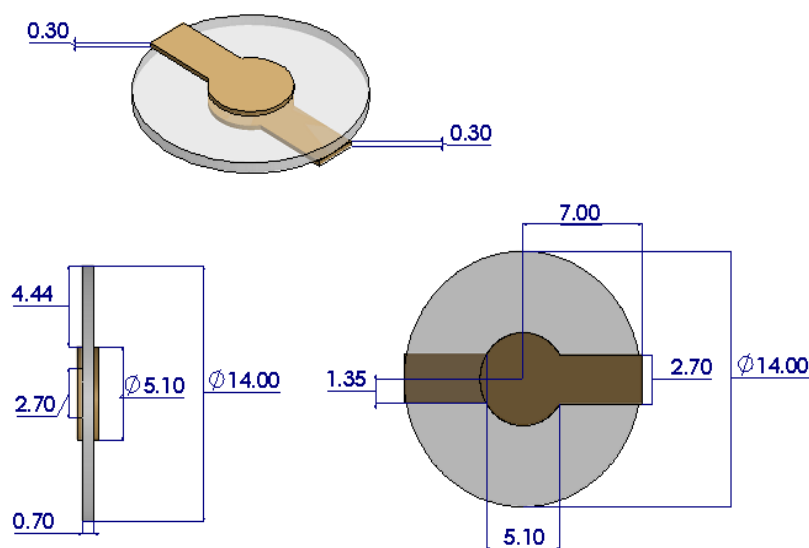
Dimensiones de la QCM, con milímetros como unidad
